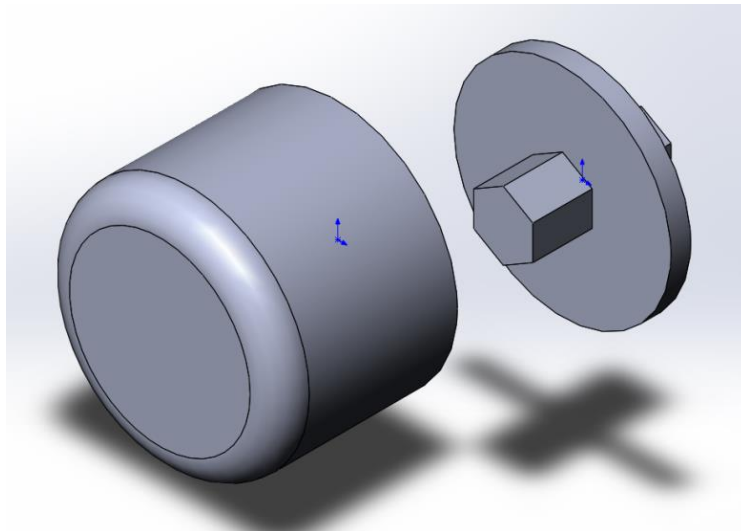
цилиндр с прокладкой на рабочем поле сборки
